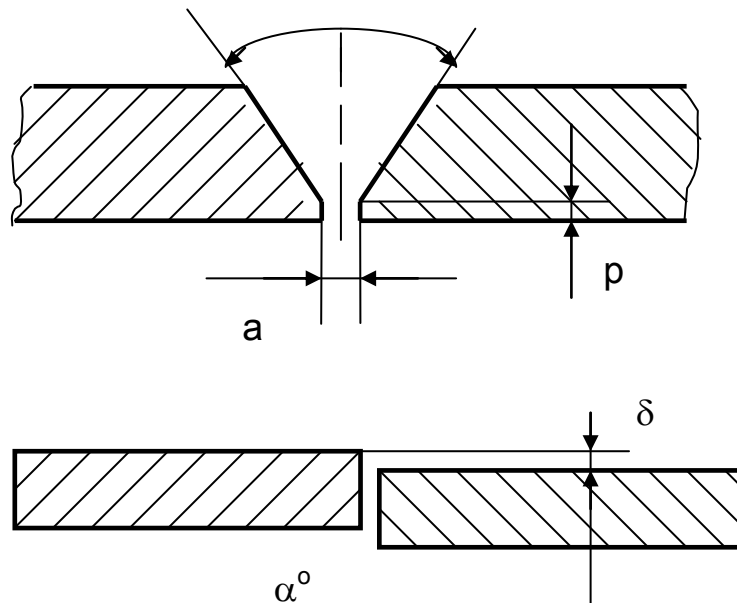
Елементи геометричної форми підготовки кромки під зварювання
